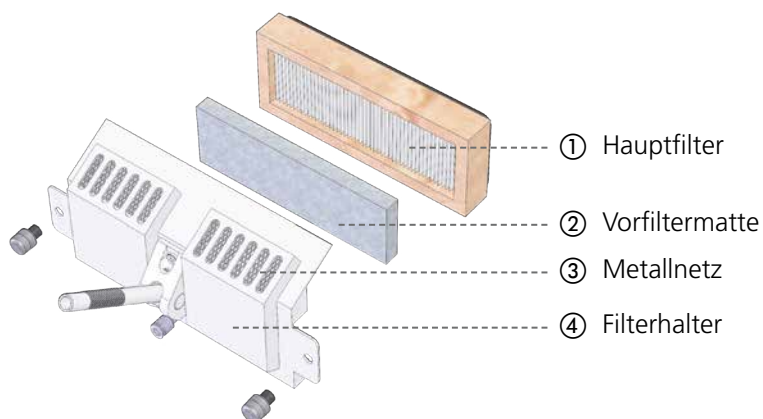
Filter der Schweißrauchabsaugung
